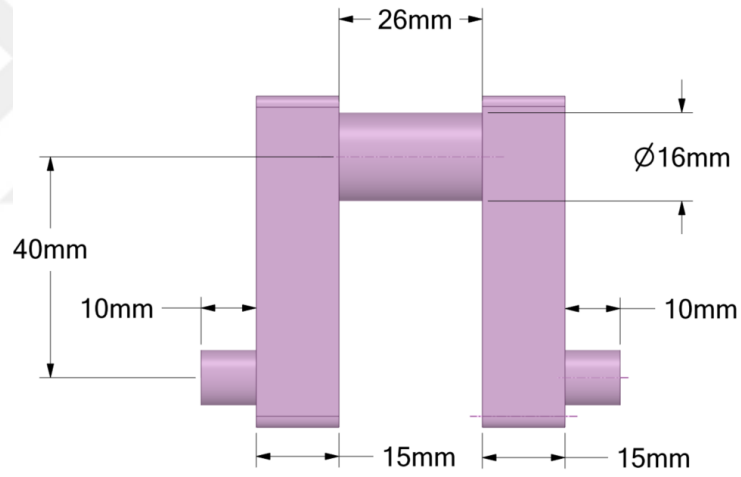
Alçak basınç kademesi krank mili boyutları
